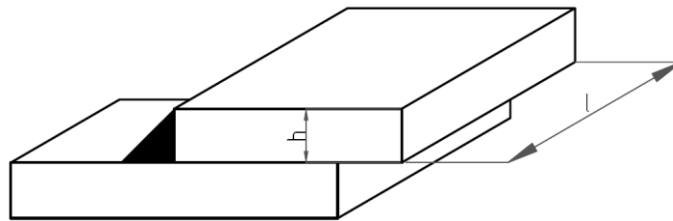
Esquema de la soldadura a filete en la bancada del motor.
